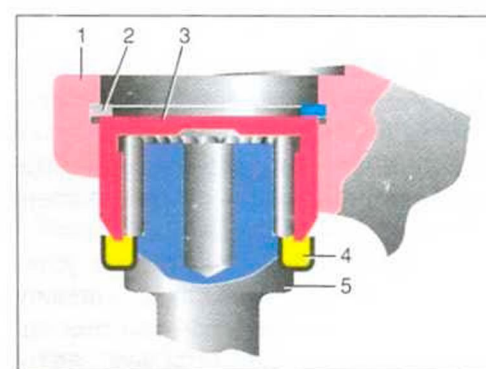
Подшипник крестовины карданного вала автомобилей ВАЗ-2101...-2107: 1 - проушина вилки; 2 - стопорное кольцо; 3 - подшипник; 4 - уплотнение; 5 - шип крестовины
